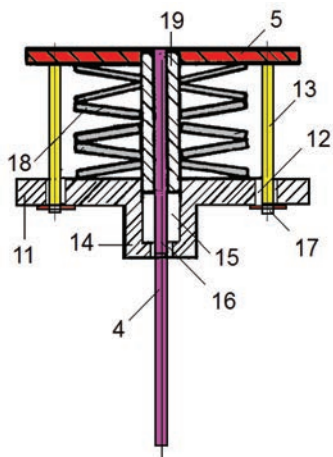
Предохранительный взрывозащитный пакет тарельчатых упругих элементов.
